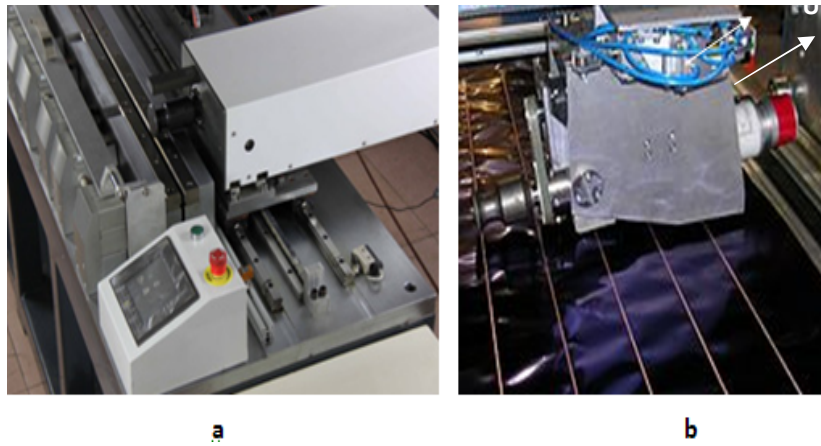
1 Bakır boru ve soğurucu tek bant kaynak makinesi
